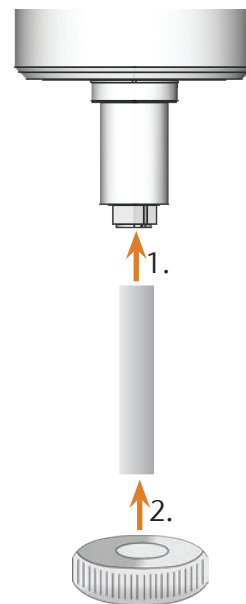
SVITAMENTO DELLA PINZA DI SERRAGGIO
